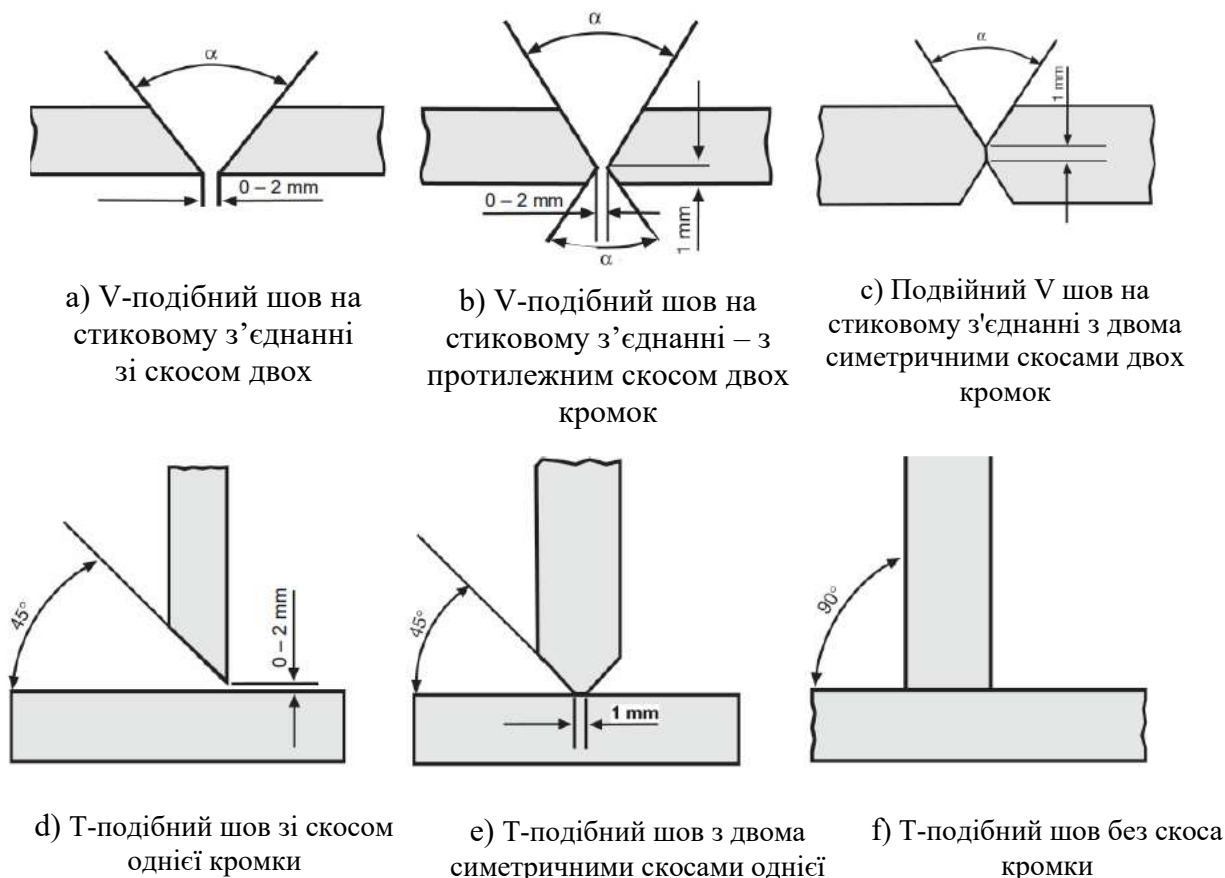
Форми обробки кромки для зварних швів
